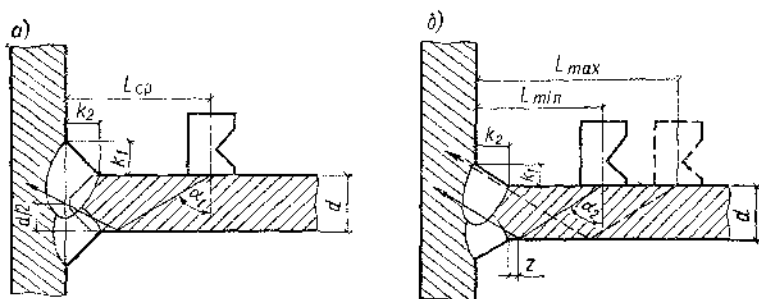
Схемы контроля тавровых сварных соединений с полным проваром
